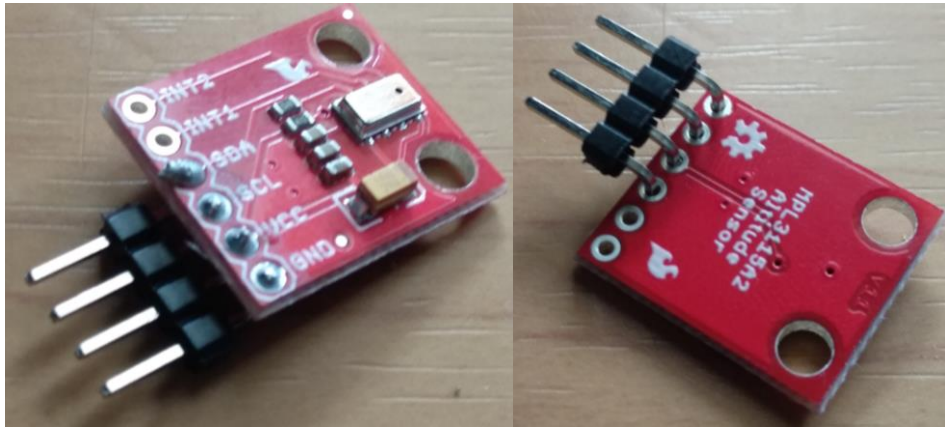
Vista superior e inferior de un sensor al que le fueron soldados pines en forma de "L".
